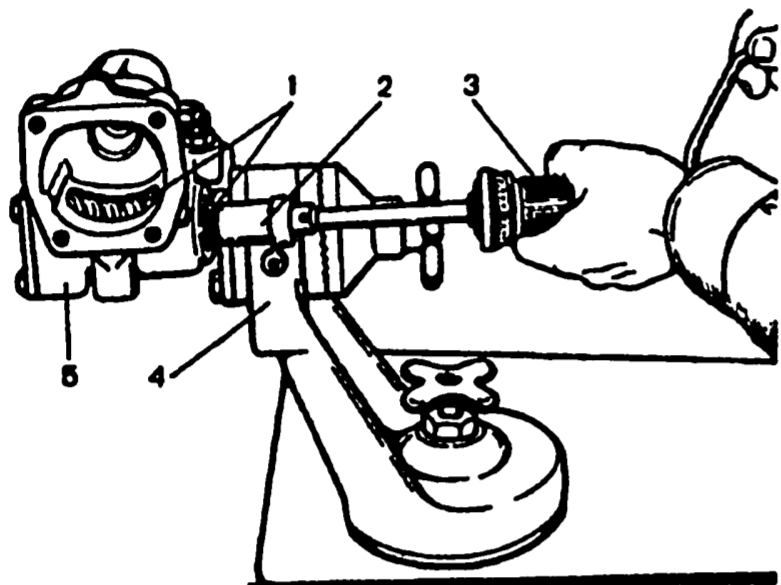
Контроль момента трения червяка динамометром: 1 - червяк; 2 - головка А.95697/5; 3 - динамометр 02.7812.9501; 4 - кронштейн стенда для ремонта картера рулевого механизма; 5 - картер рулевого механизма.
